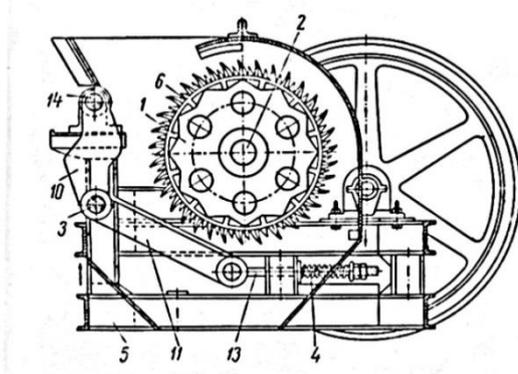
Одновалковая зубчатая дробилка: 1 – зубчатый валок; 2, 7 – центральный и приводной вал; 3 – шарнирное крепление колосниковой решетки; 4 – пружина; 5 – станина; 6 – зубцы, 8 – колосники; 9 – зубчатая передача; 10, 11 – решетка; 12 – приводной шкив; 13 – тяга
